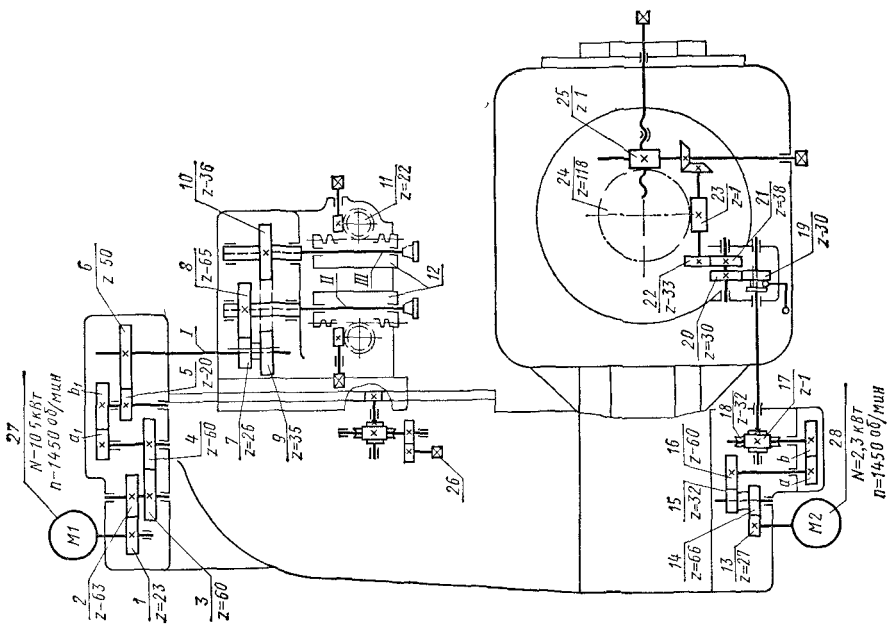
Кинематическая схема карусельно-фрезерного станка
